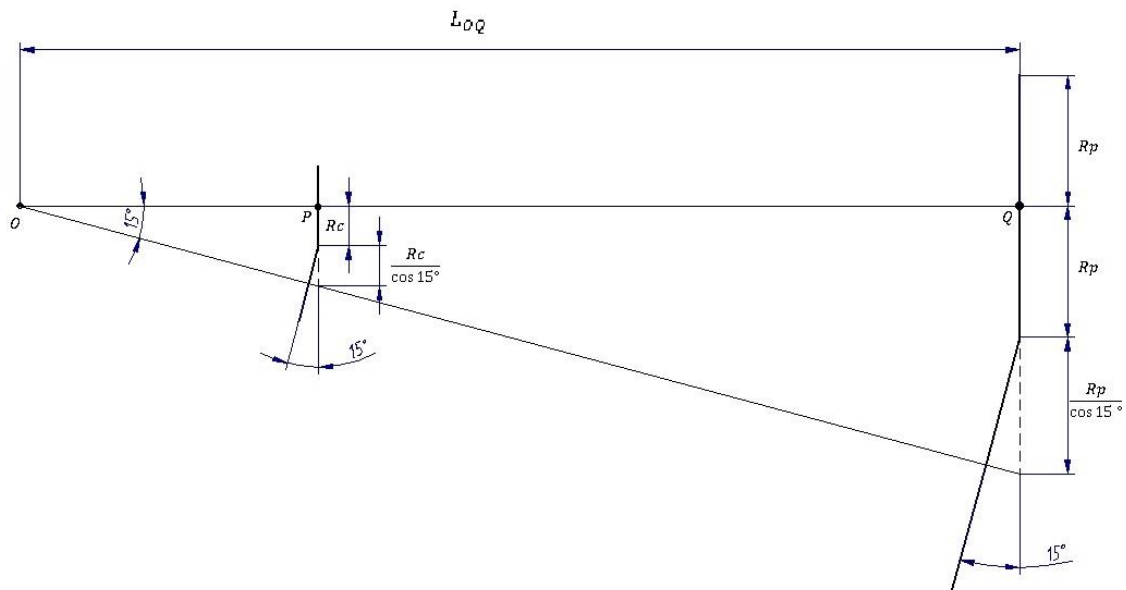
Disposición geométrica de las cuchillas y los engranajes sobre el eje.
